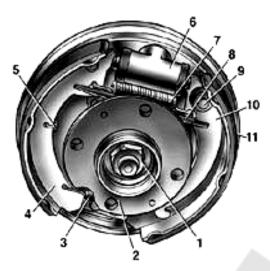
Барабанный тормозной механизм: 1 — гайка крепления ступицы; 2 — ступица колеса; 3 — нижняя стяжная пружина колодок; 4 — тормозная колодка; 5 — направляющая пружина; 6 — колесный цилиндр; 7 — верхняя стяжная пружина; 8 — разжимная планка; 9 — палец рычага привода стояночного тормоза; 10 — рычаг привода стояночного тормоза; 11 — щит тормозного механизма
